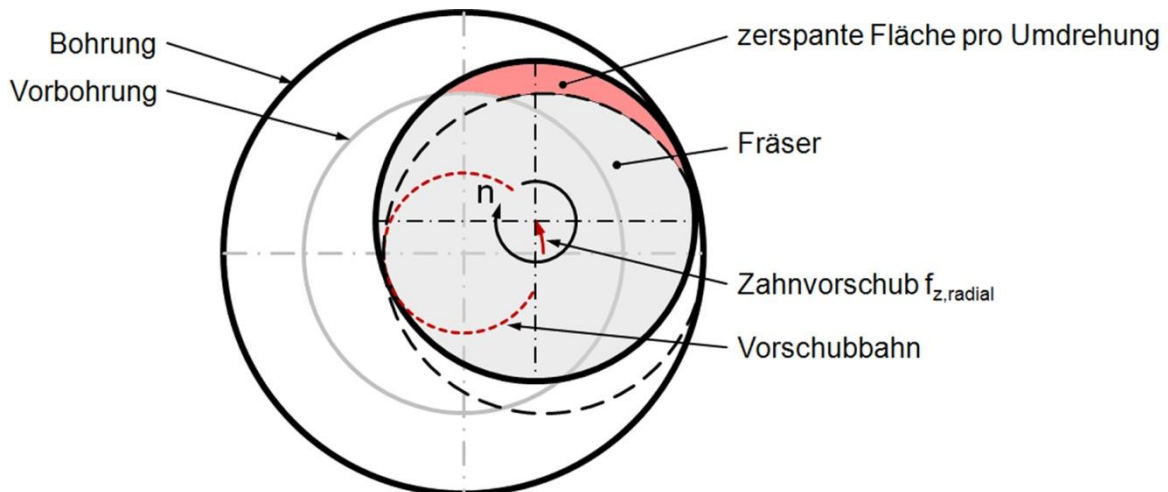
Schematische Darstellung der analysierten Fräsbearbeitung bei Bearbeitung der Werkzeugaustrittsseite
